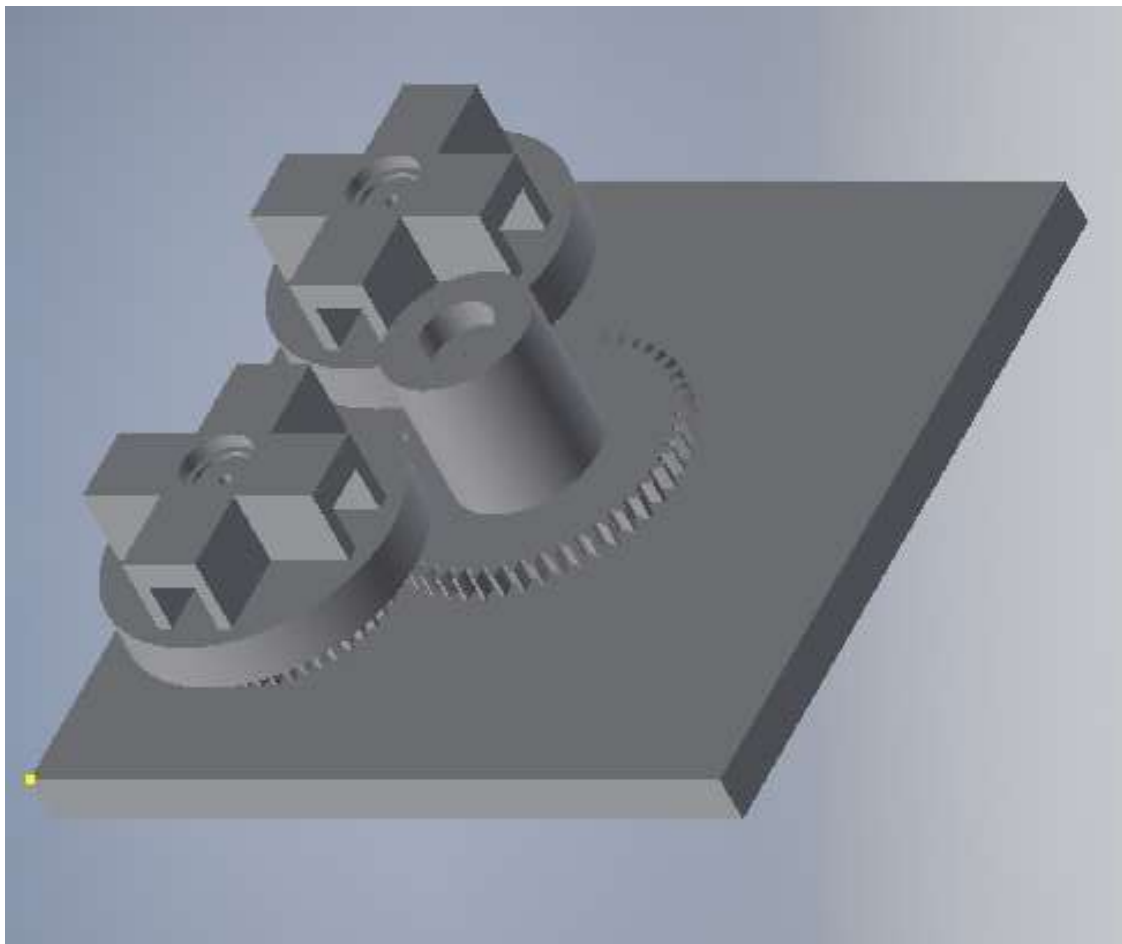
Vista isométrica del ensamblaje del sistema con enlace mecánico.
